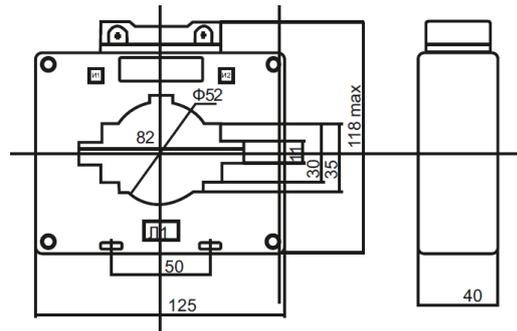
Габаритные и установочные размеры трансформаторов тока ТШП-0,66-80
